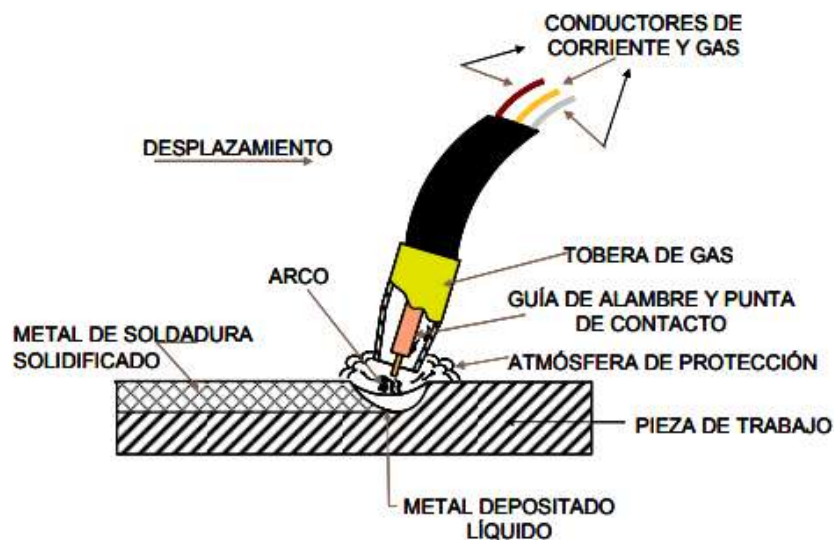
Esquema del proceso de soldadura GMAW [8].
